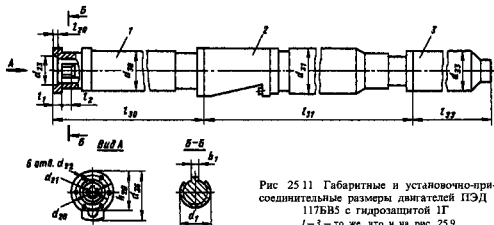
11 Габаритные и установочно-при- соединительные размеры двигателей ПЭД 117БВ5 с гидрозащитой ПГ 1—3 — то же, что и на рис 25 9
